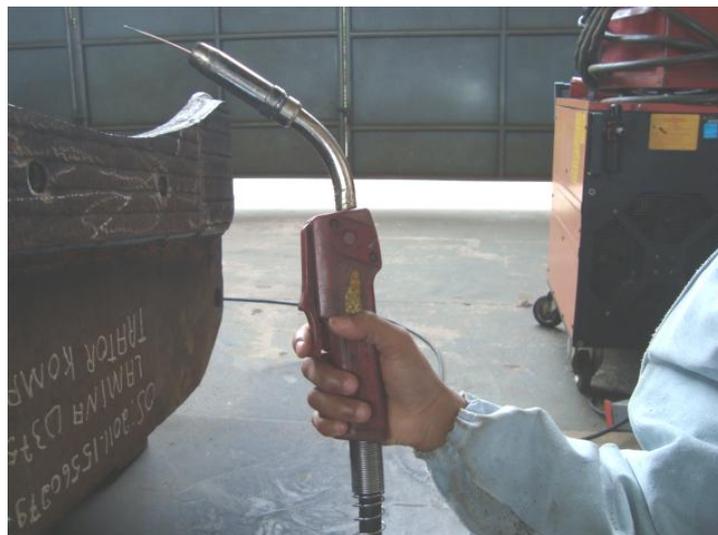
Ferramenta (tocha) de soldagem tipo MIG.
